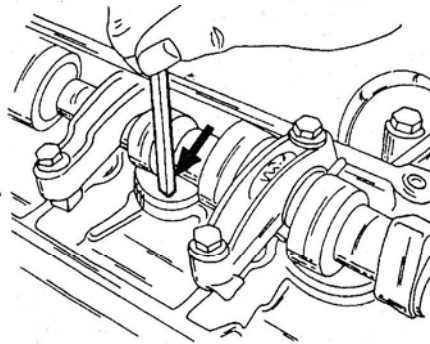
Проверка толкателя при недостаточной подаче масла или других дефектах.
